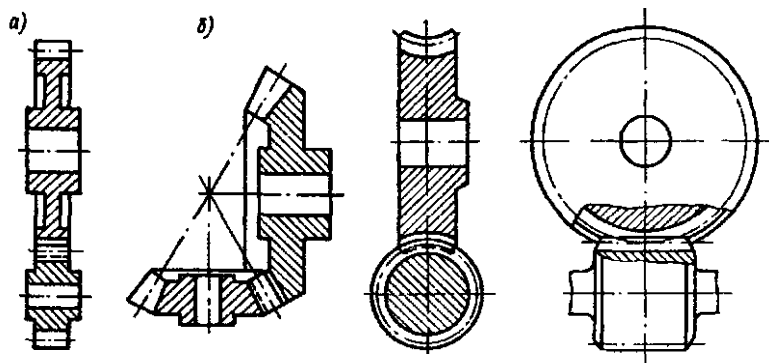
Продольный разрез зубчатых передач: *a* — цилиндрической; *б* — конической
